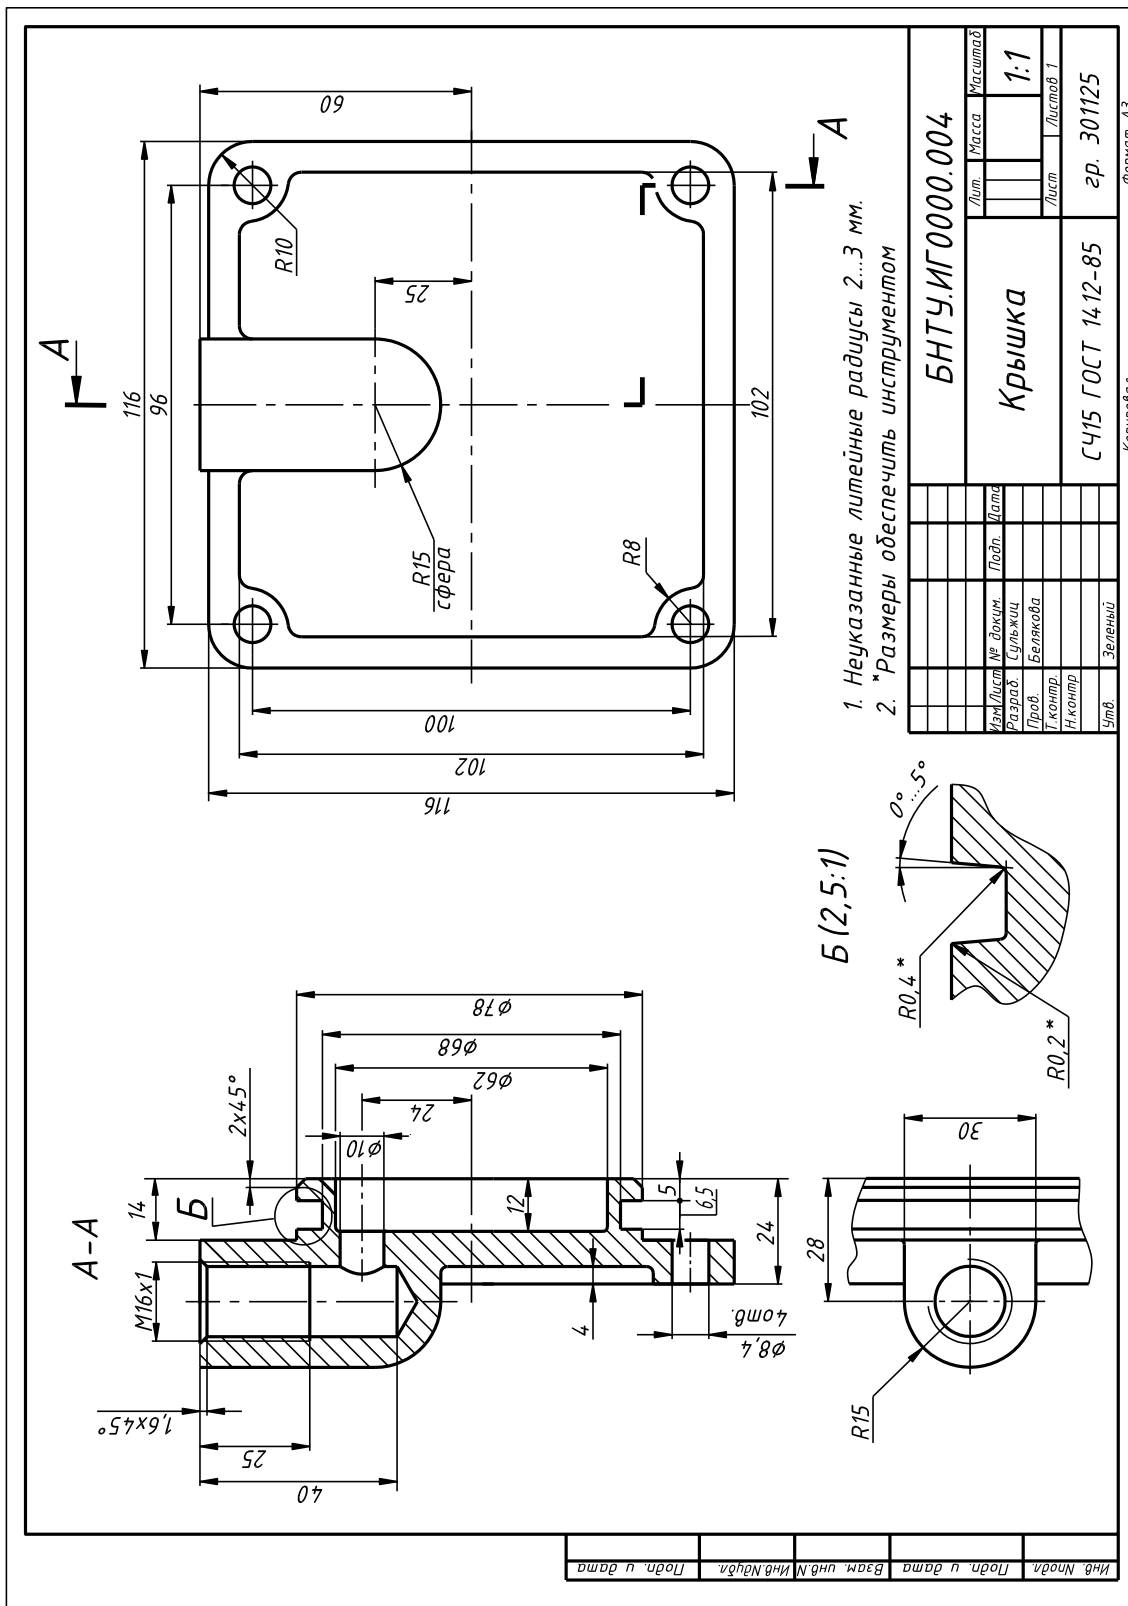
Чертеж крышки с квадратной формой фланца: выполнен ступенчатый разрез, чтобы в разрез попало крепежное отверстие
